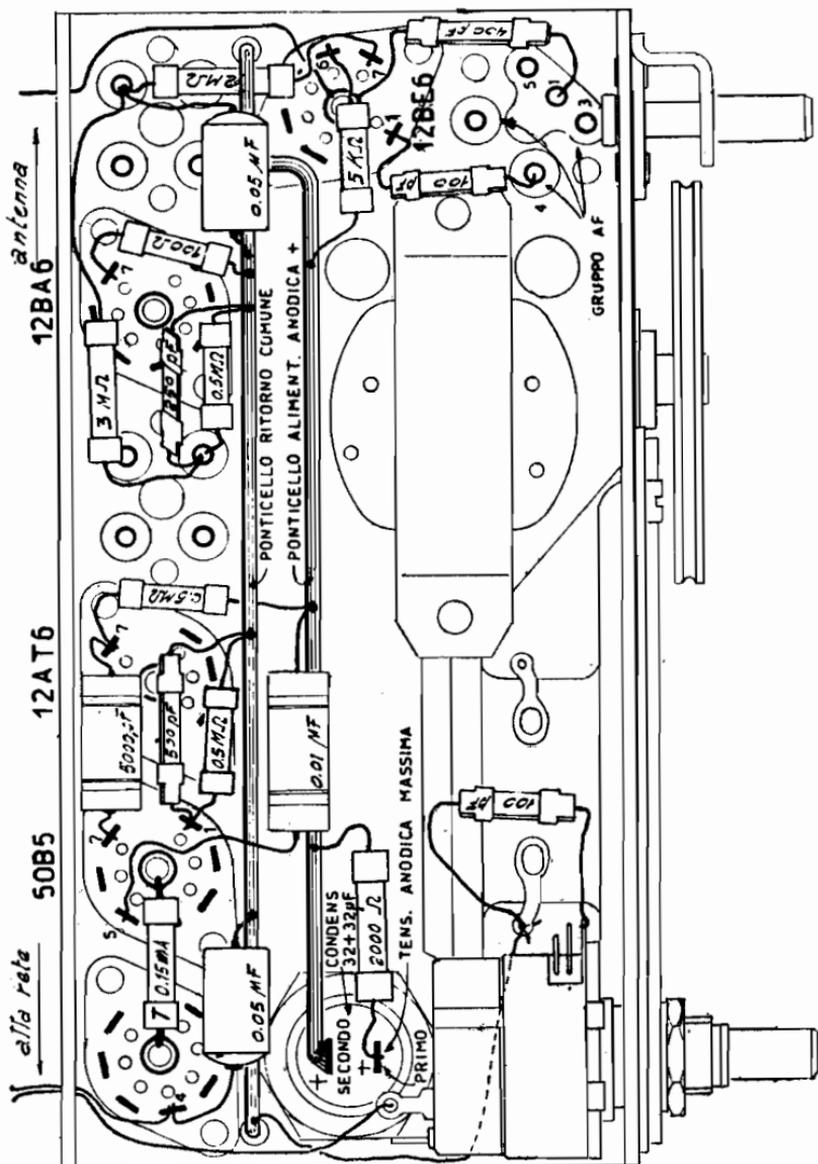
Seconda fase del montaggio sotto il telaio.
